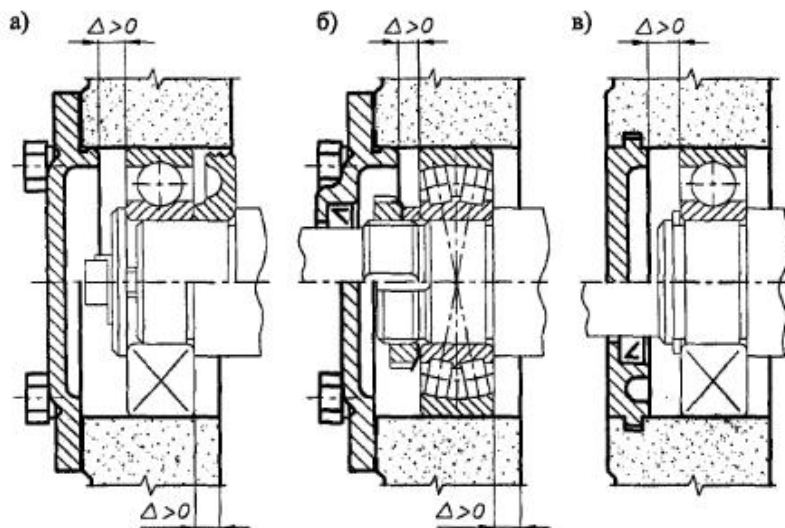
Установка наружного кольца неразъемного подшипника в корпусе плавающей (самоустанавливающейся) опоры
